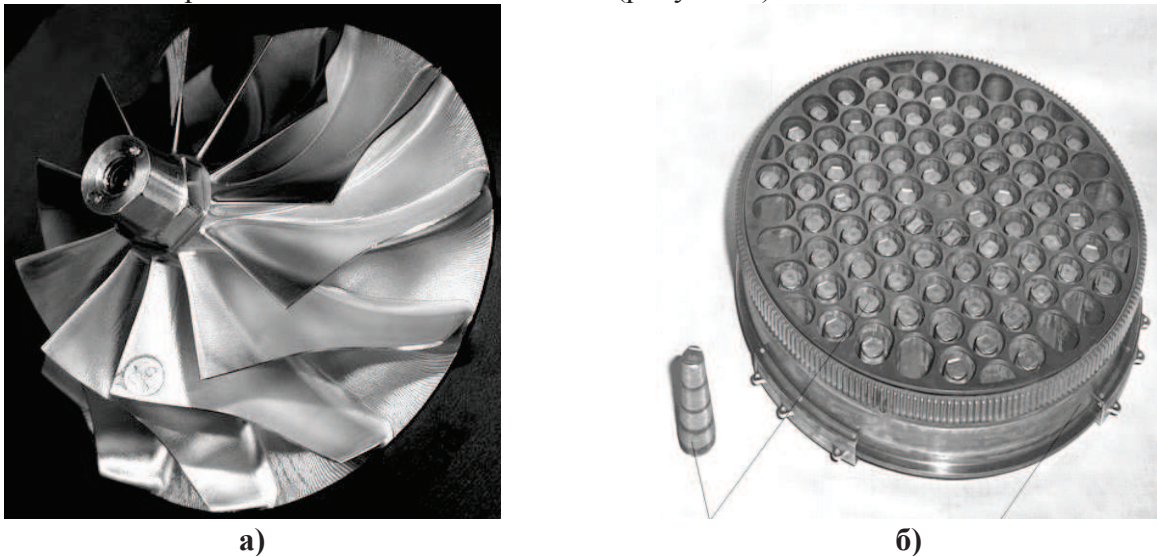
Ротор компрессорной ступени (а), корпус вращающегося рекуперативного теплообменника (б) из стали
